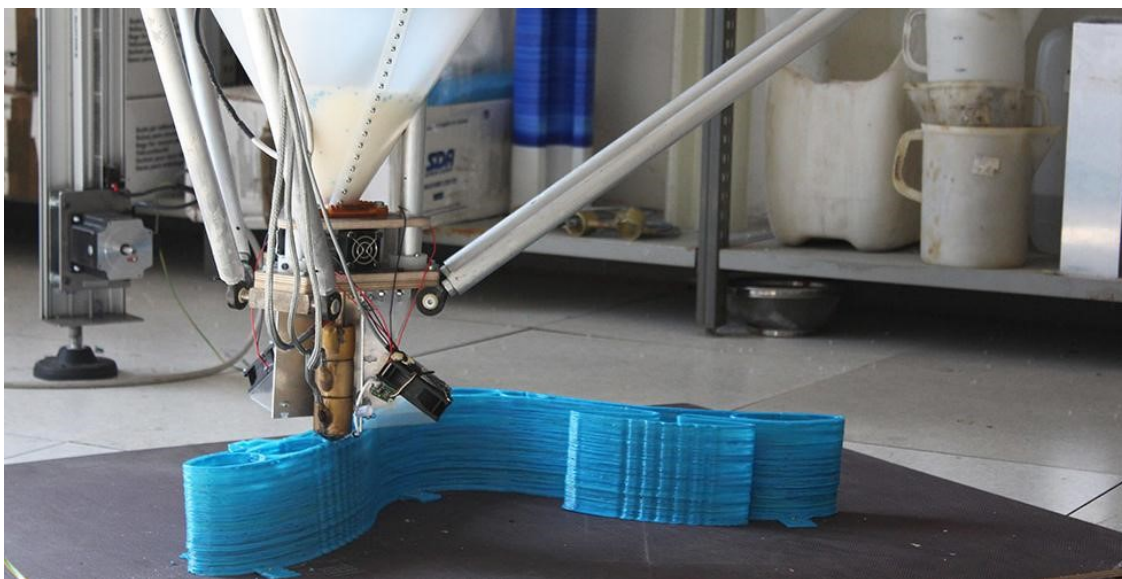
Granulový extruder Direct 3D převzato z [16]
